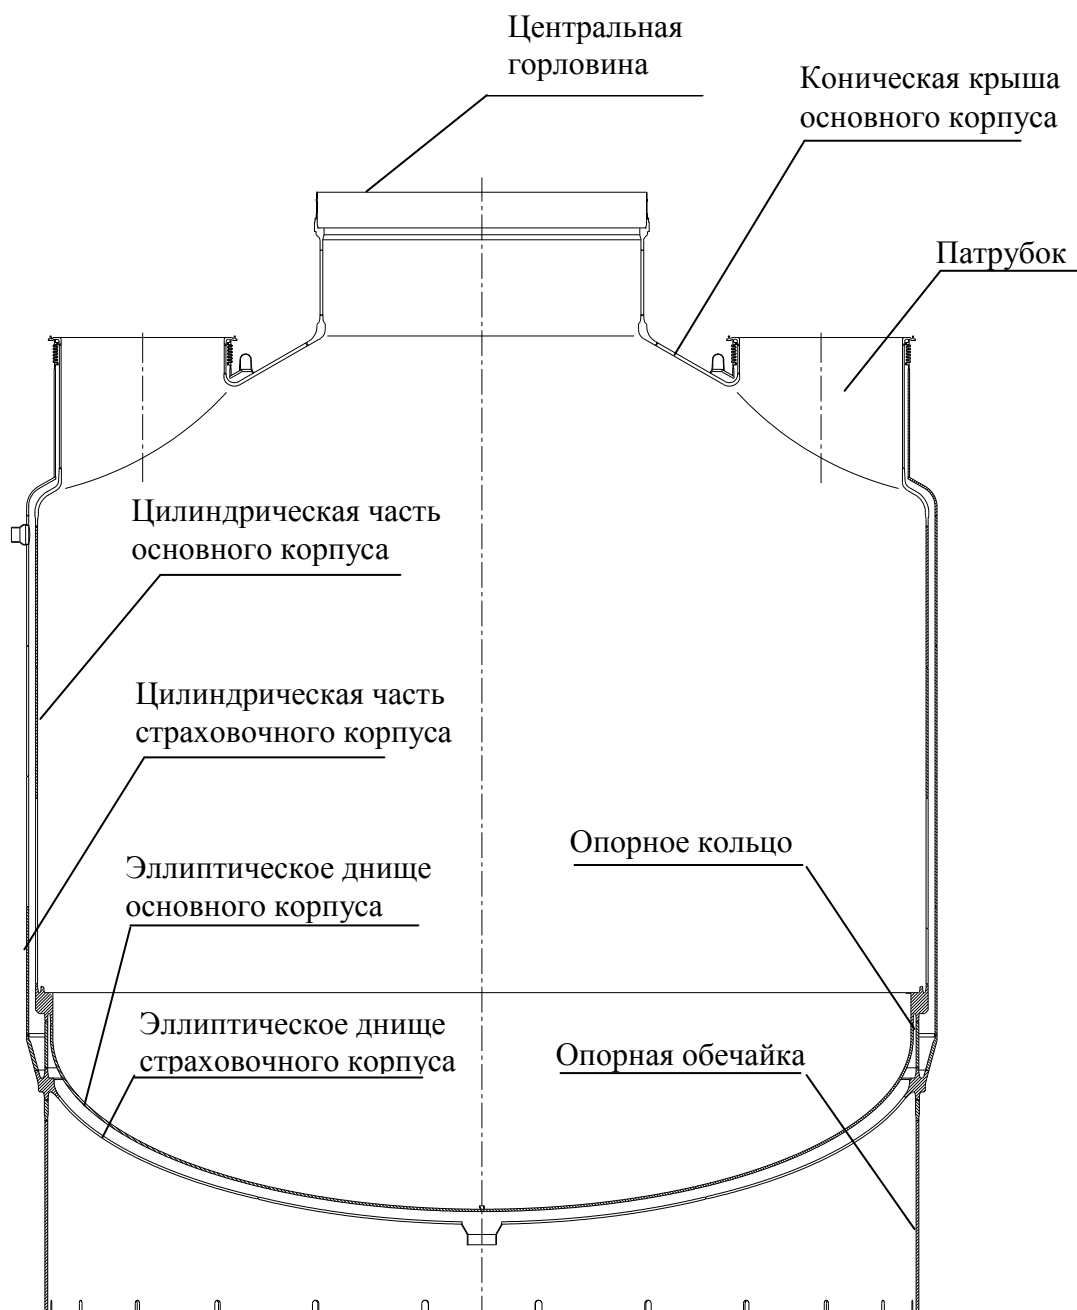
Конструктивная схема основного и страховочного корпусов реактора БН-800
